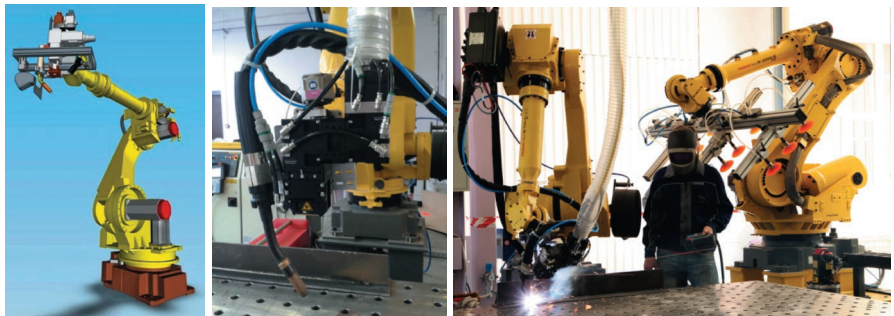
Роботизированный комплекс для гибридной лазерно-дуговой сварки судовых микропанелей.
